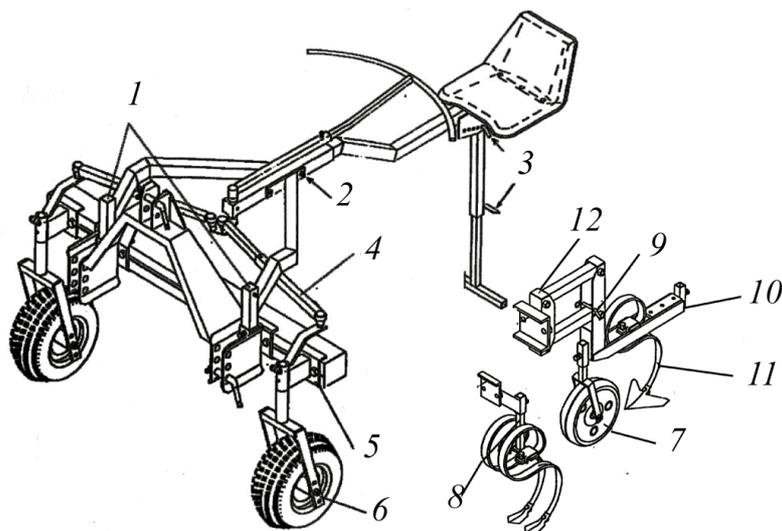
Несущая рама и рабочие секции культиватора GC «Egedal»: 1 – место установки опрыскивающей или подкормочной секции; 2 – рулевой механизм; 3 – сидение оператора; 4 – регулируемые поперечные тяги; 5 – механизм регулировки колеи; 6 – управляемые колеса с механизмом регулирования положения по высоте; 7 – копирующее колесо рабочей секции; 8 – секция для рыхления следа опорных колес; 9 – блокировочный штифт; 10 – место крепления рабочих органов; 11 – универсальная лапа; 12 – копирующая рельеф местности рабочая секция
